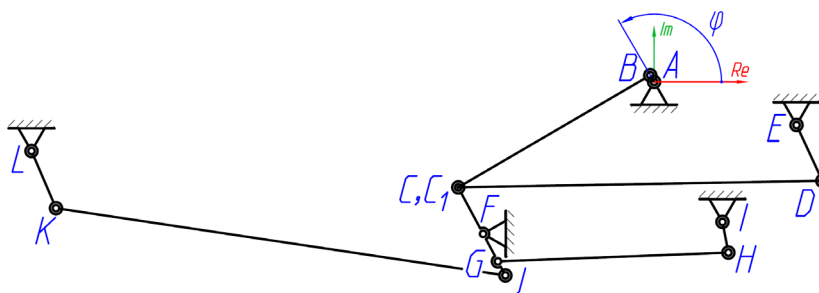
Кинематическая схема механизма привода очистки зерноуборочного комбайна
